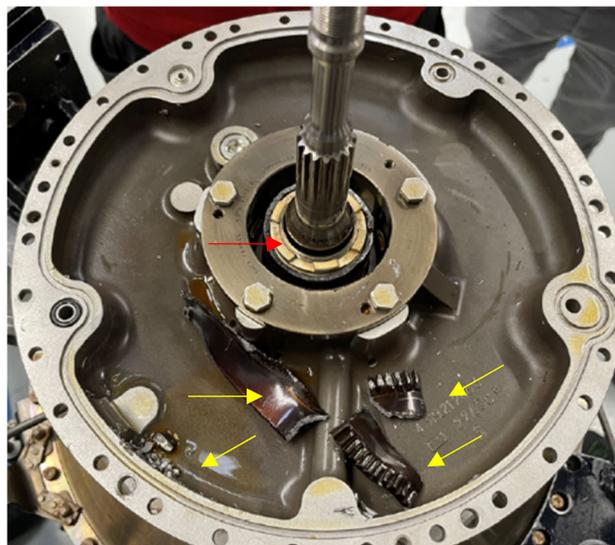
Rückseite der *Accessory Gearbox* mit den Bruchstücken des Antriebszahnrades (gelbe Pfeile) und dessen Hauptkörper (roter Pfeil)
